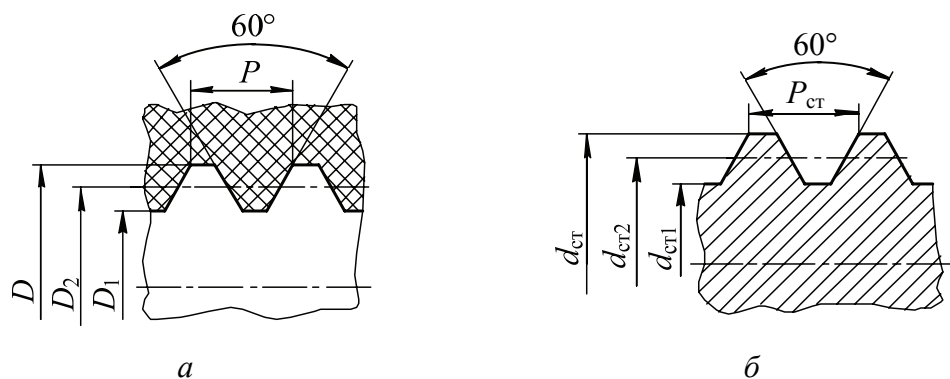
Гайка (а) и резьбоформирующий стержень (б)
